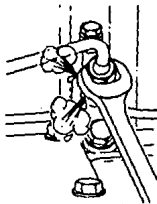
Conexión que une a la línea de alta presión con el inyector.
